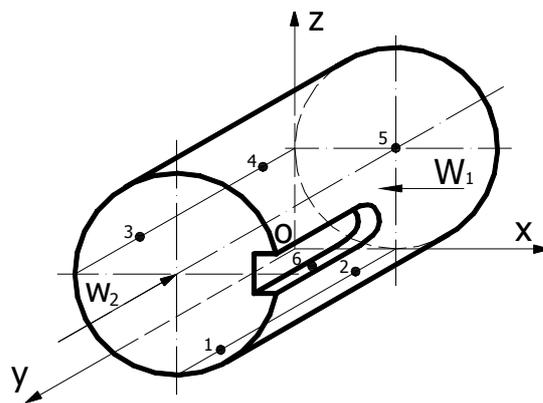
Схема установки длинной цилиндрической детали.
